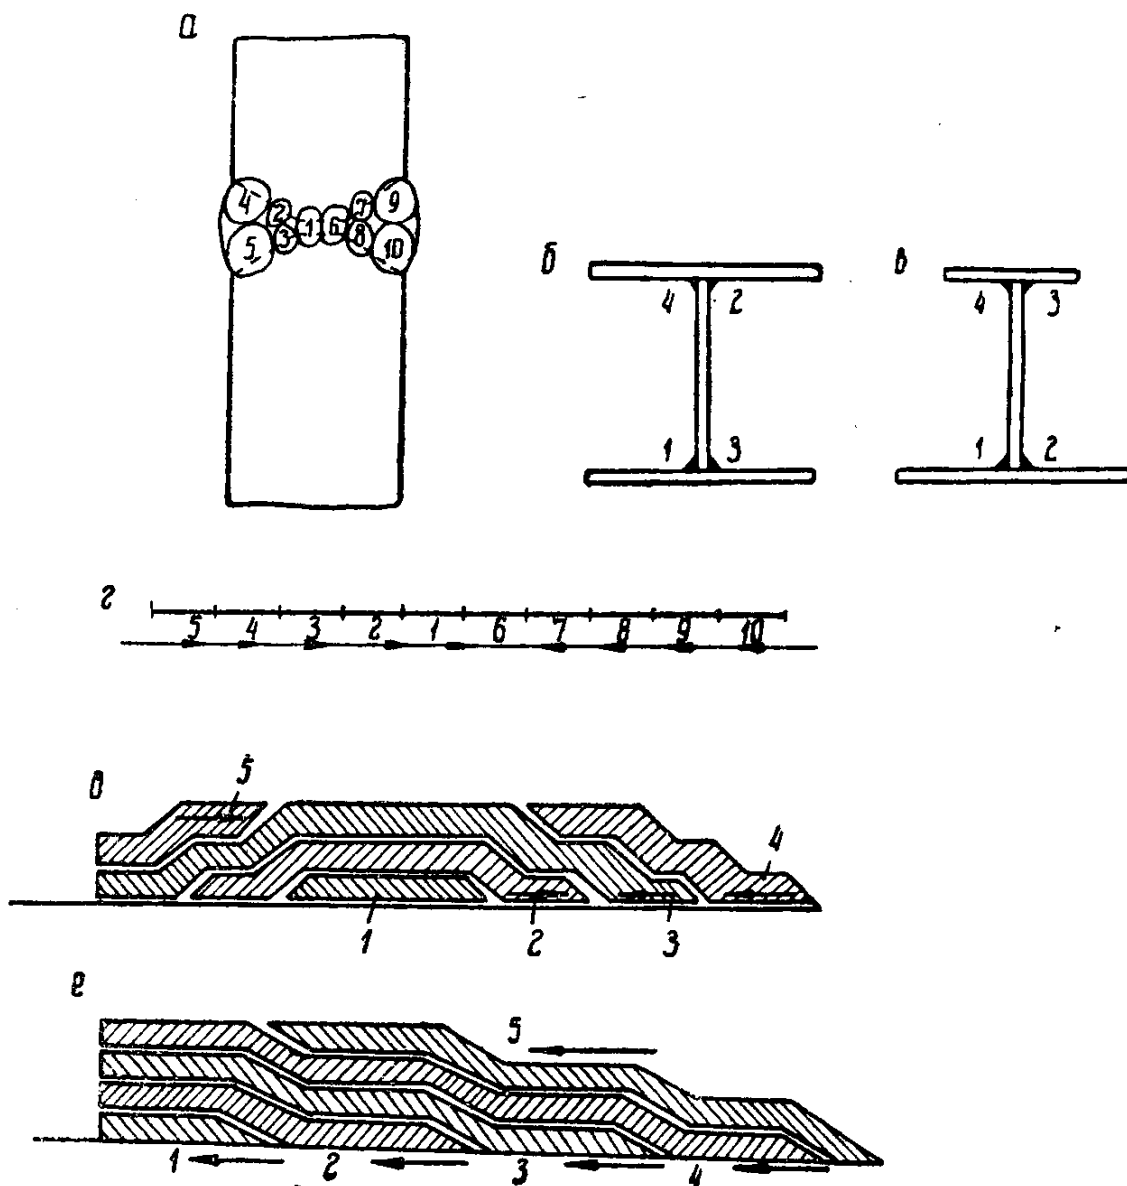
Порядок наложения швов и способы сварки:
